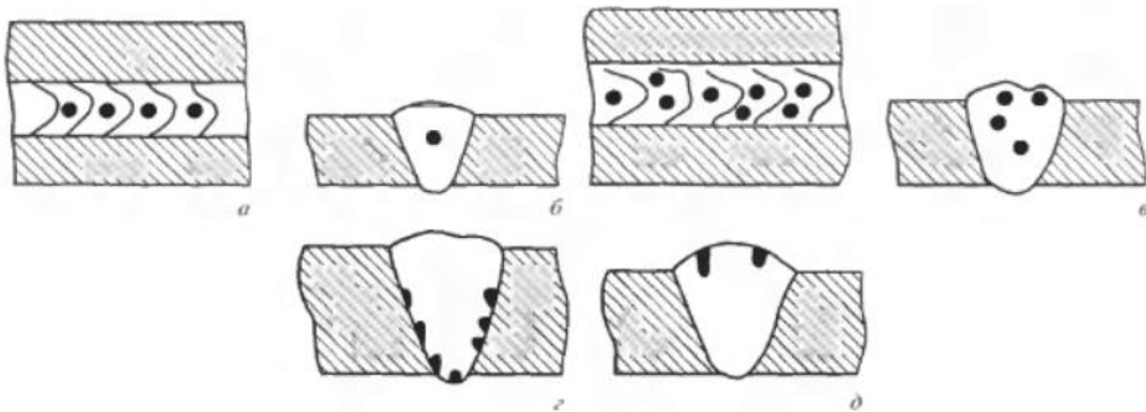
Эскиз дефекта сварного шва
